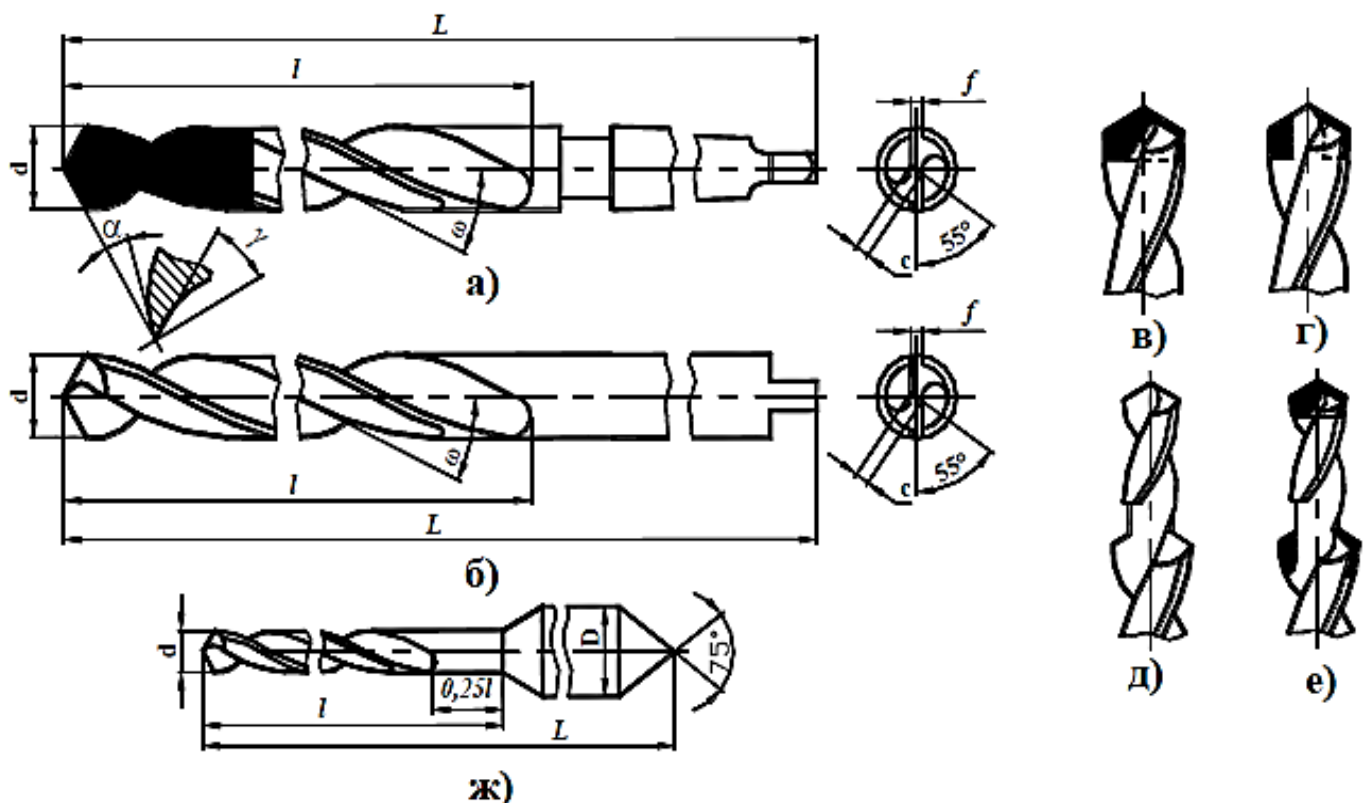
Стандартні спіральні свердла: а) зварне з конічним хвостовиком; б) цілісне з циліндричним хвостовиком; в) з цілісною напаяною твердосплавною пластинкою; г) з напаяними роздільними твердосплавними пластинками; д) ступінчасте з швидкорізальної сталі; е) ступінчасте з напаяними твердосплавними пластинками; ж) з потовщеним циліндровим хвостовиком. d - діаметр свердла; L - довжина інструменту; l - довжина робочої частини; α - задній кут; γ - передній кут; ψ - кут нахилу перемички, $\psi = 55^\circ$; f - ширина допоміжної стрічки; ω - кут нахилу гвинтової канавки; c - довжина перемички (товщина серцевини інструменту); d - діаметр хвостовика.
